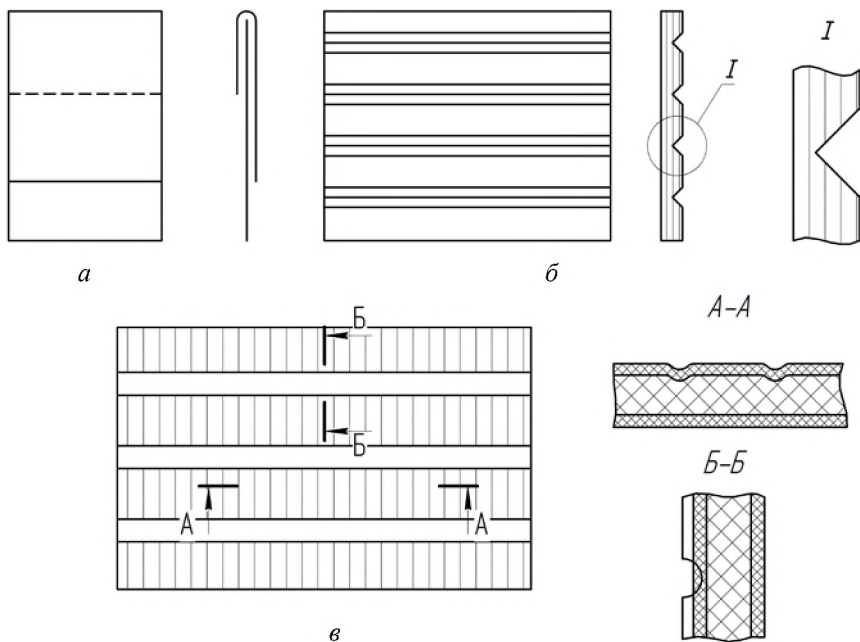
Типы флегматизаторов: а – листовый; б – рифленый; в – пластинчатый
